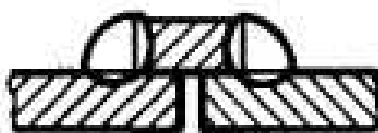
Сварное муфтовое соединение труб [2]
